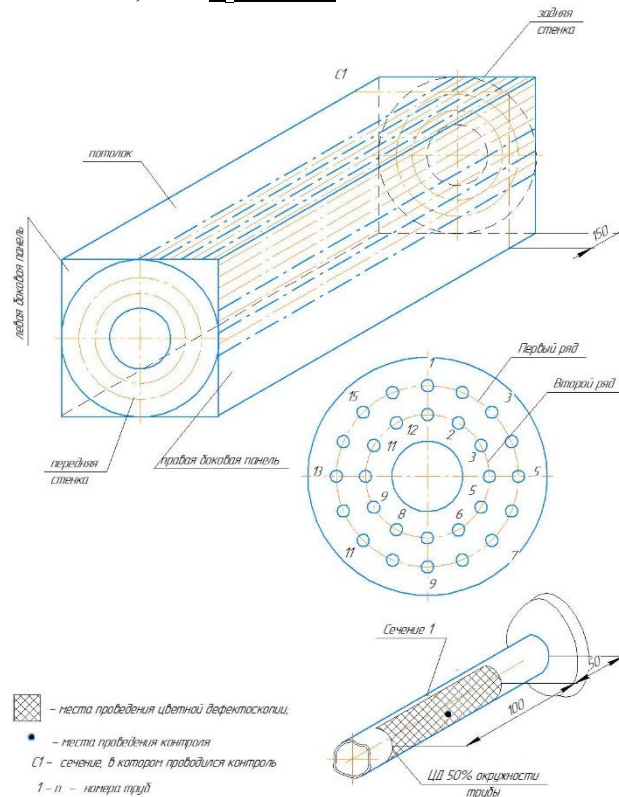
Контроль сварных швов методом УЗК, контроль толщины стенки, ЦД котла «КСВа-1,0Гс».
